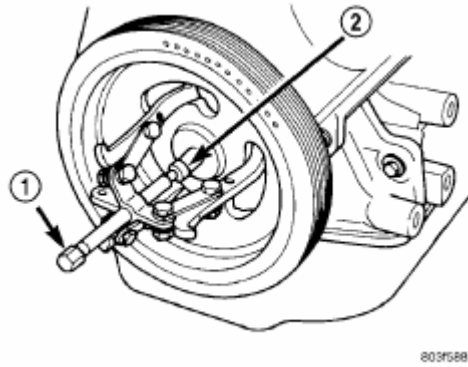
Снятие гасителя вибрации коленчатого вала – типовое.
